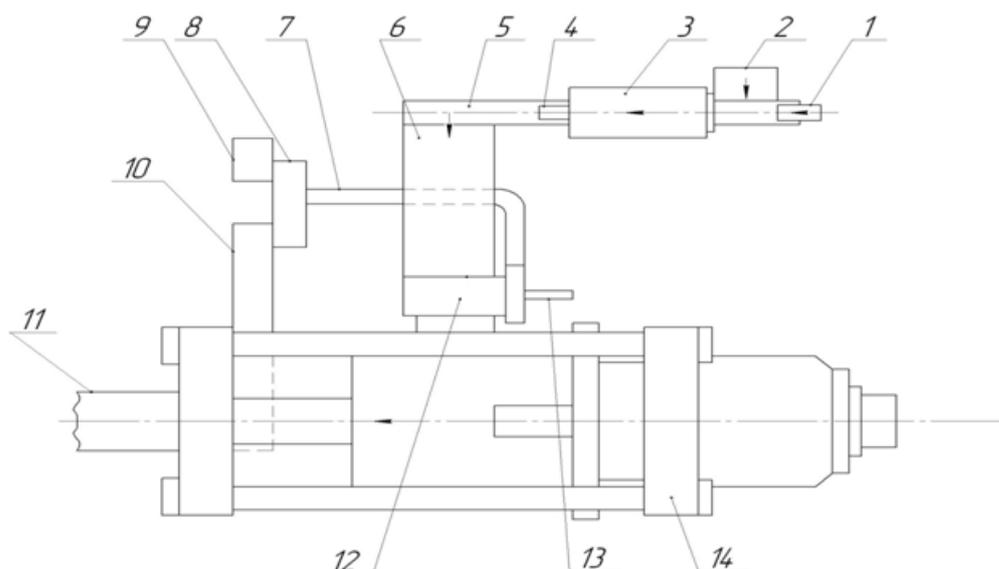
Механизмы гидропресса для выполнения вспомогательных операций: 1– толкатель слитков; 2–стол загрузки слитков в печь; 3–индукционная печь; 4–приемник нагретых слитков; 5–рольганг; 6–наклонный столик; 7–передатчик пресс-шайб; 8– устройство для разделения пресс-шайбы и пресс-остатка; 9–бункер для пресс-состатков; 10–устройство для отделения пресс-остатка от матрицы; 11–приемный стол пресса; 12–податчик слитков; 13–устройство для подачи пресс-шайбы на податчик; 14–пресс.
